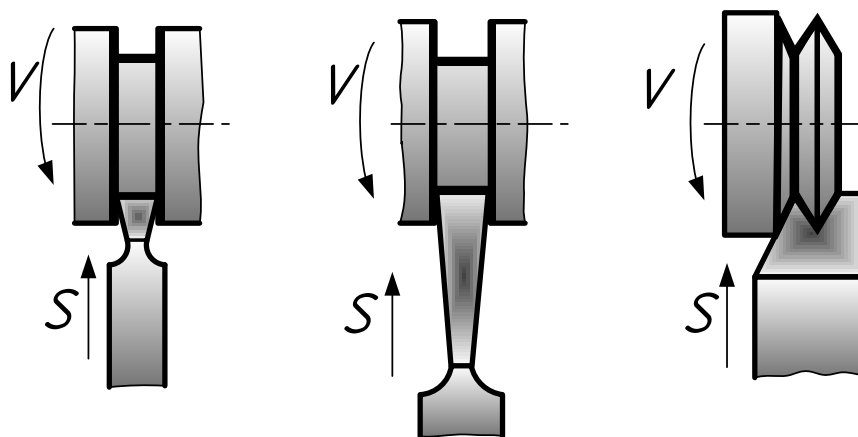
Обработка отрезными, канавочными и фасонными токарными резцами
